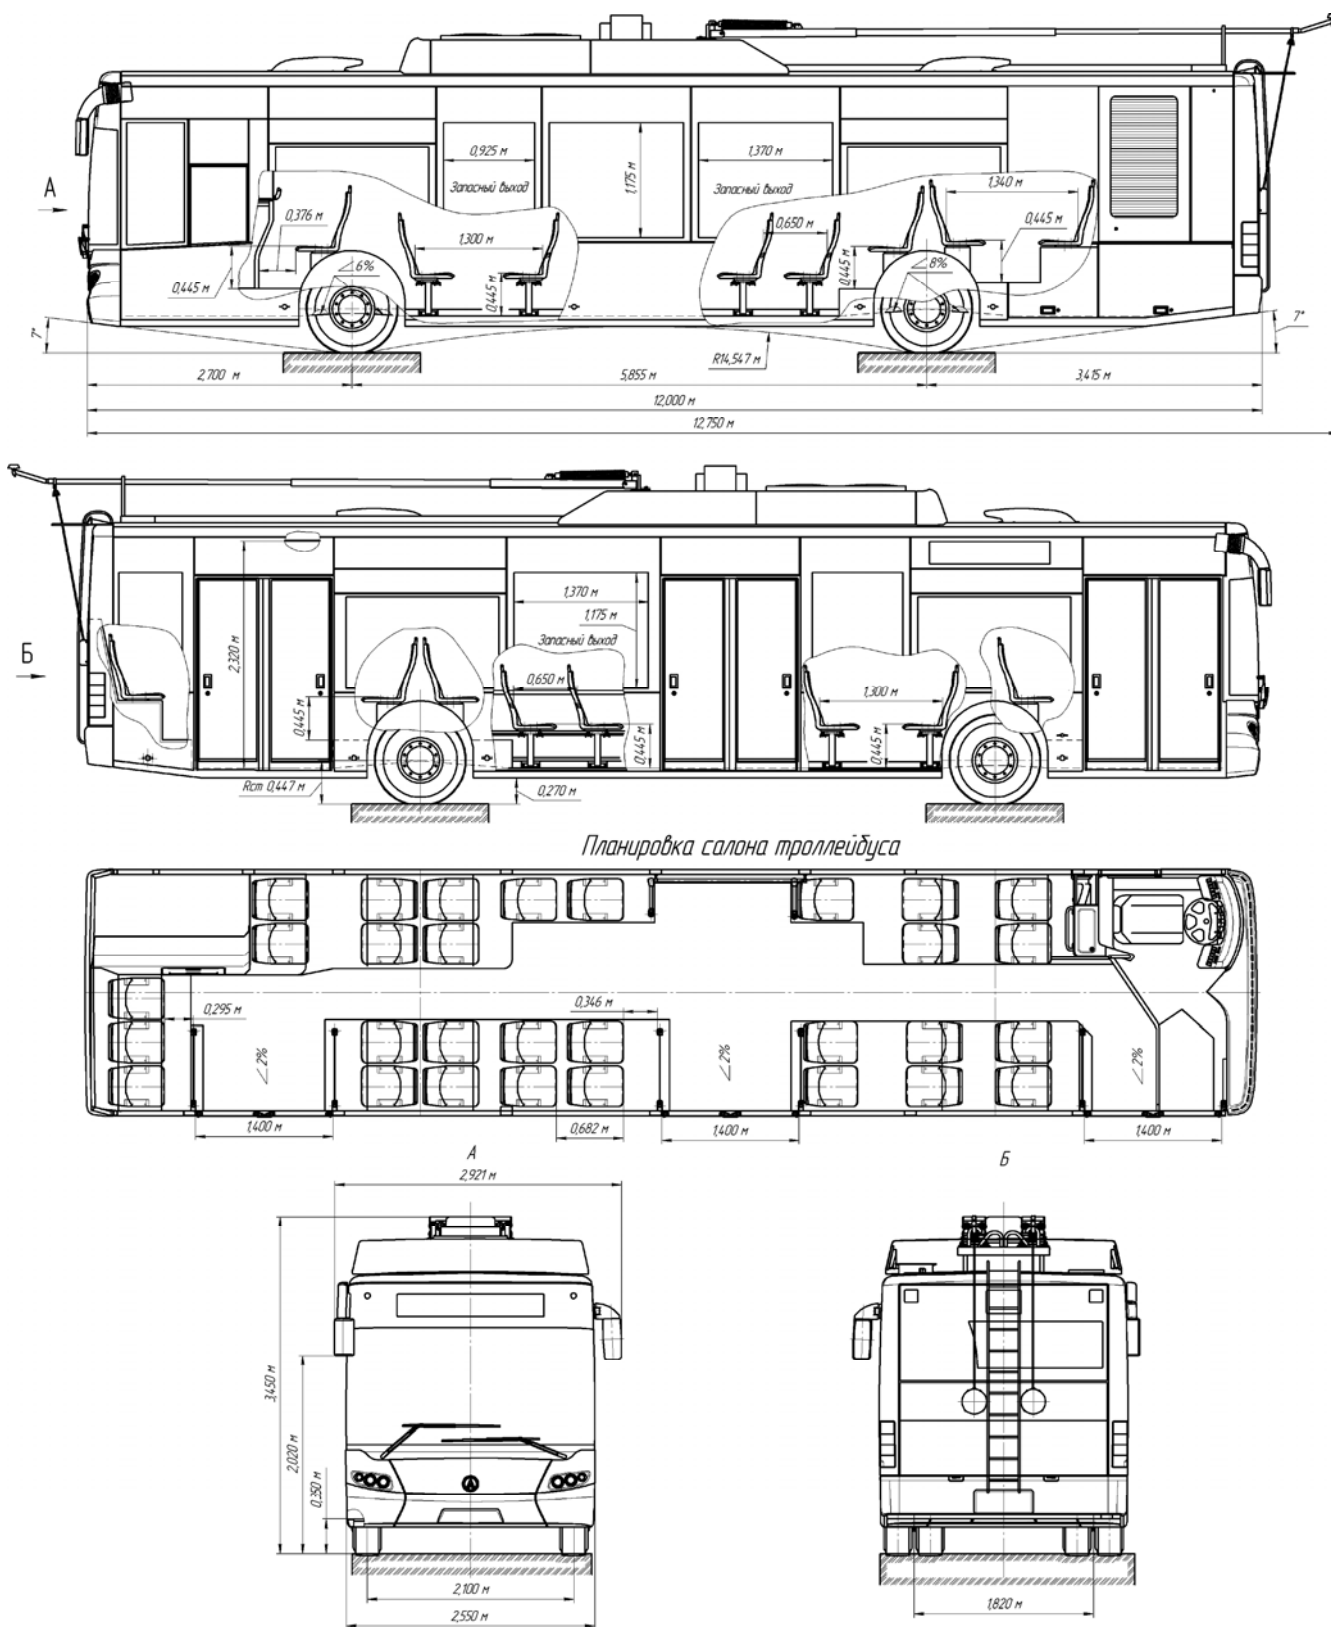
Планировка салона и габаритные размеры троллейбуса
